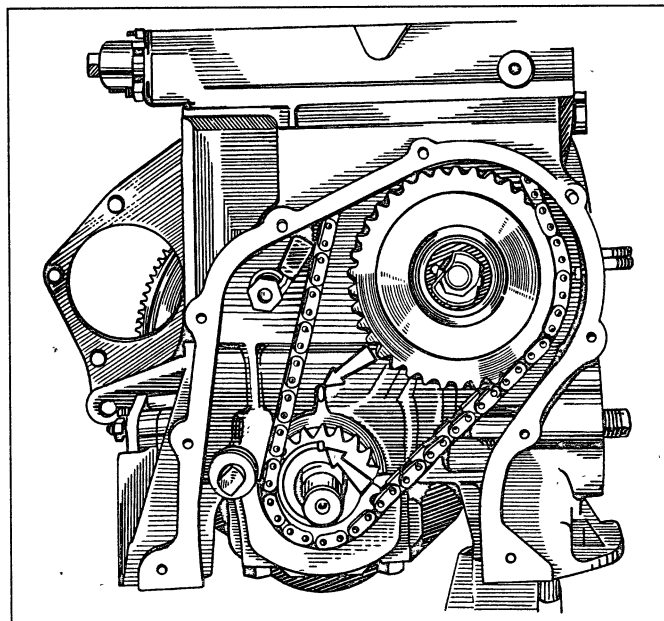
Проверка совпадения установочной метки на звездочке коленчатого вала с меткой на блоке цилиндров
